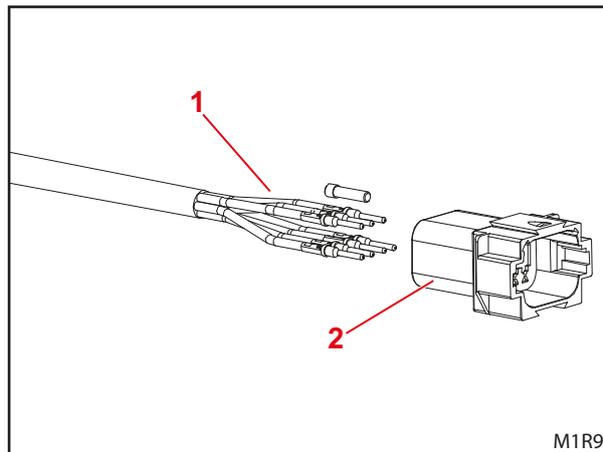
8-контактный штекерный разъем без выступов для установки в нижний узел Hydro-Fix
